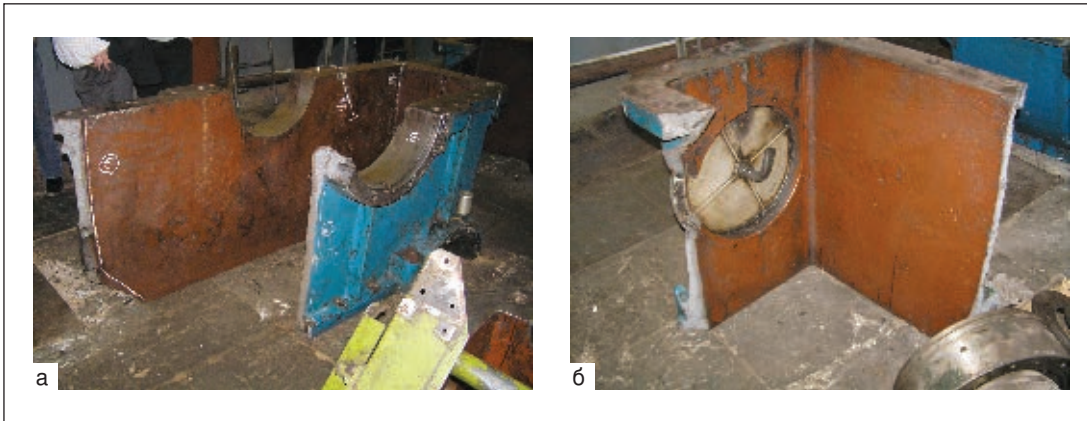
Общий вид разрушенной средней части корпуса редуктора А-1100: а — основная часть корпуса редуктора; б — отломанный фрагмент корпуса редуктора
